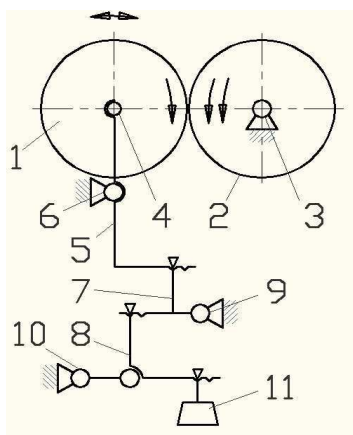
Конструкция установочного механизма с рычагами первого рода
